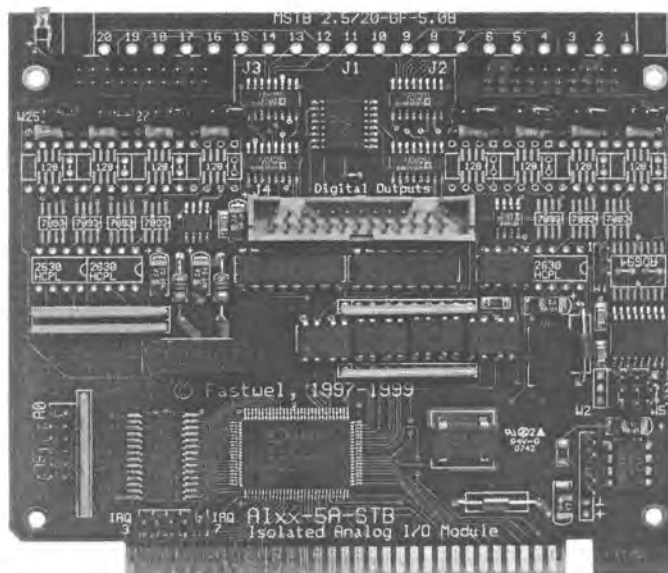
Внешний вид платы AI16-5A-1 с измерительными преобразователями
